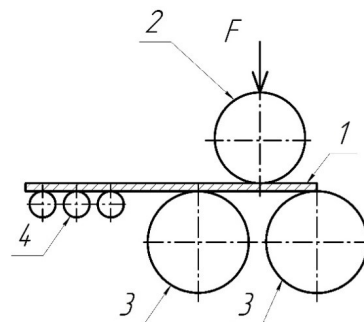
Установка заготовки на станок: 4 — дополнительные (поддерживающие заготовку) валки
